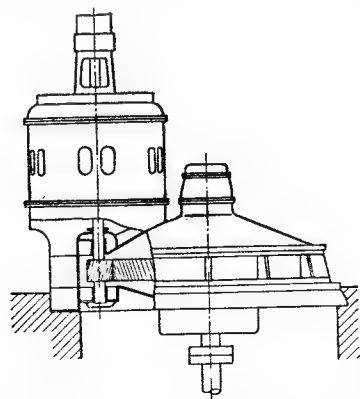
Цилиндрический редуктор между вертикальными валами турбины и генератора.
